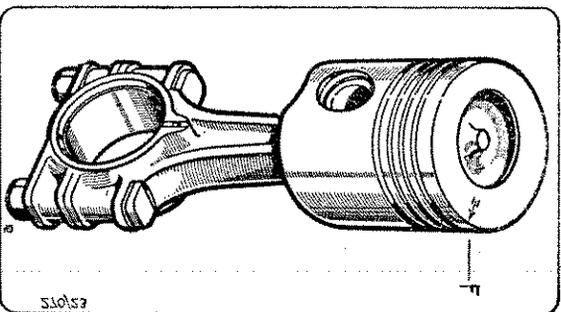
RIFERIMENTO MON-TAGGIO PISTONE
